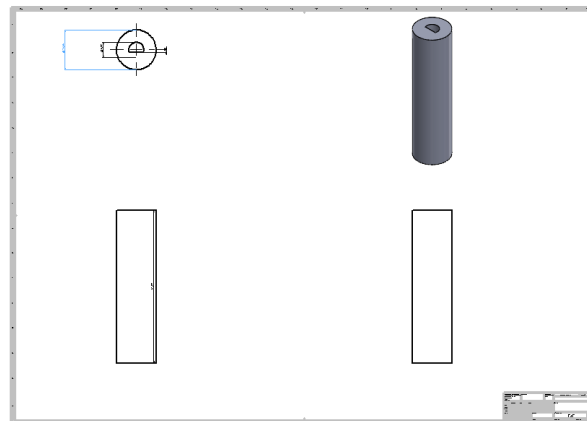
Perspectiva isométrica y vistas diédricas de la pieza 5.
